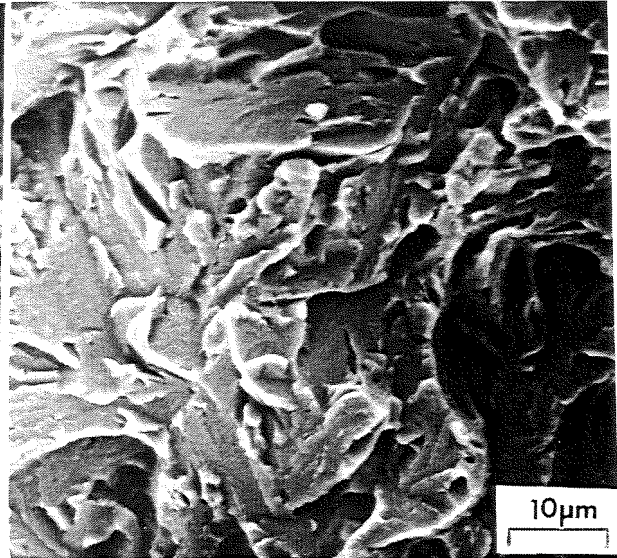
Spaltflächen eines transkristallinen Trennbruches
